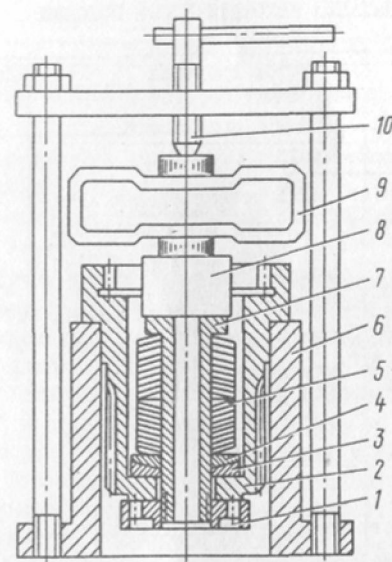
Сборочный узел для предварительного нагружения пакета тарельчатых пружин
